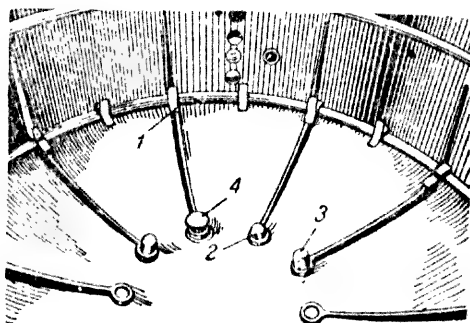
Задняя часть барабана с деталями крепления отражателя (вид изнутри):
